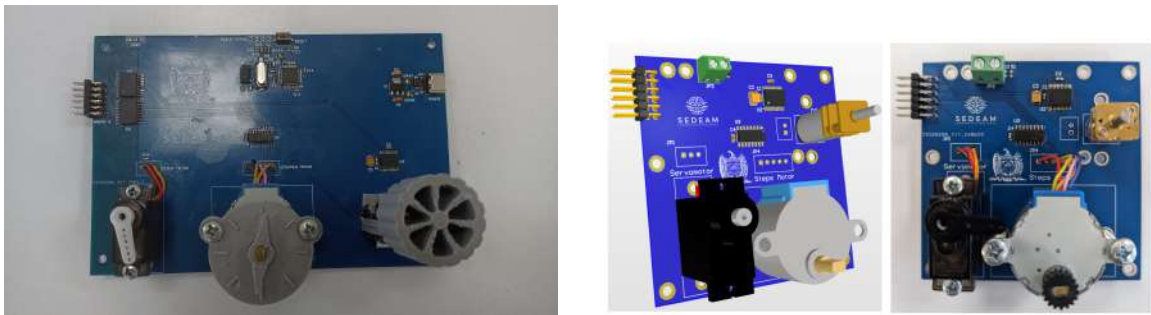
Izquierda: Nueva PCB ensamblada. Derecha: Versión anterior del diseño con motores conectados.
